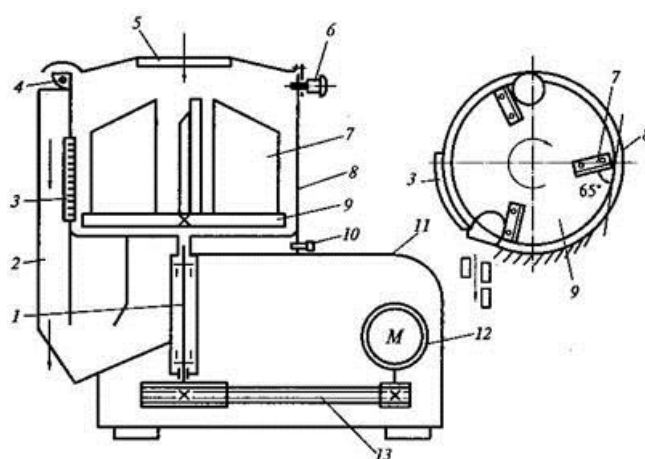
Схема роторной овощерезательной машины МРО 400-1000: 1 – вал; 2 – разгрузочный канал; 3 – ножевой блок; 4 – ось; 5 – загрузочная воронка; 6 – фиксатор; 7 – лопасти; 8 – рабочая камера; 9 – диск; 10 – защелка; 11 – корпус; 12 – электродвигатель; 13 – клинременная передача.
